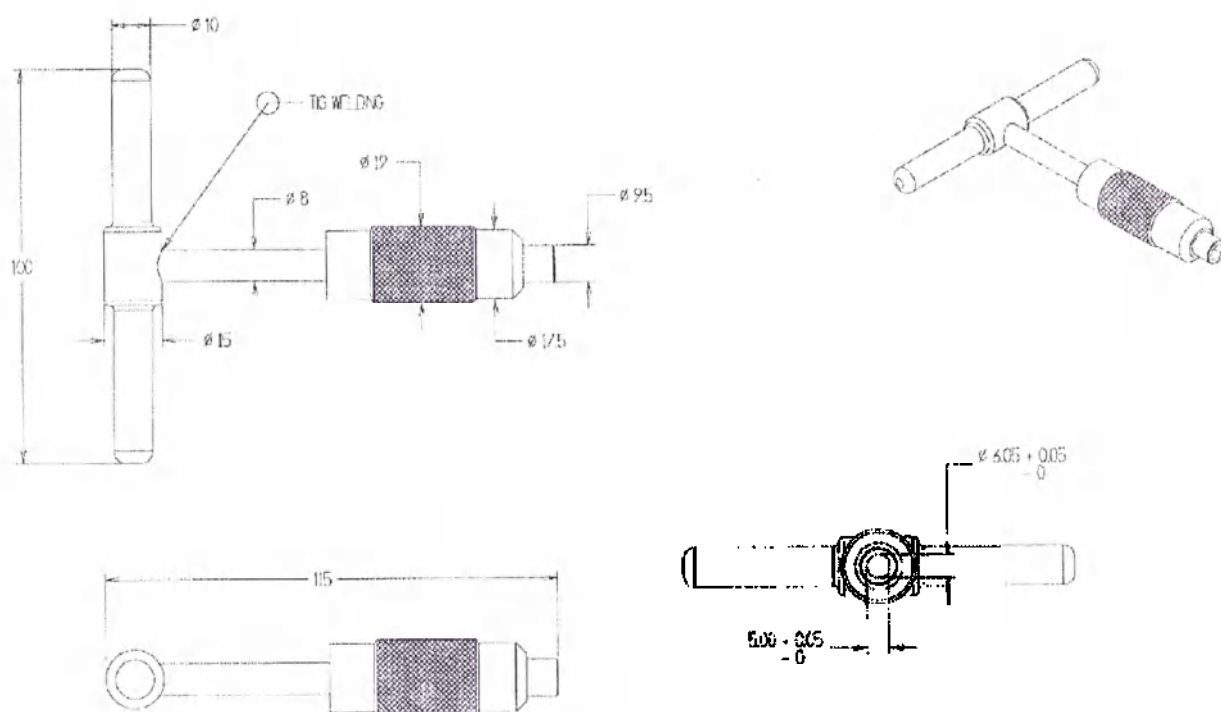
Рукоятка Т-образная для насадок, ID-17-0051
